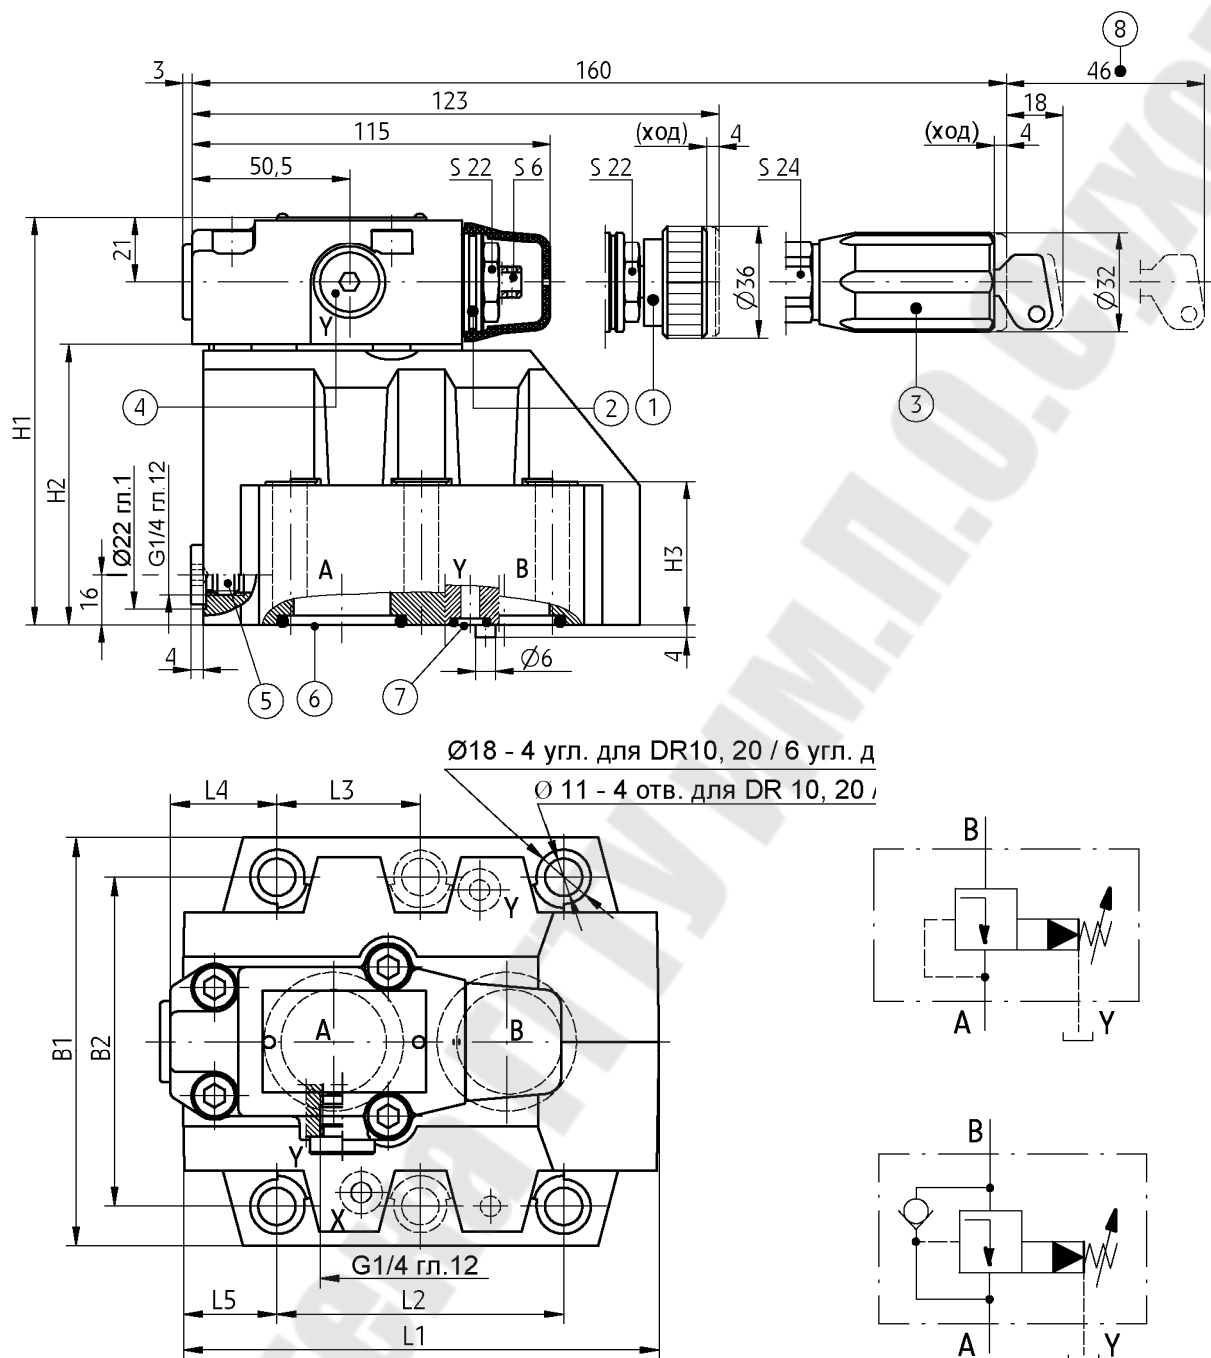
Общий вид, схемы и габаритные размеры редукционного клапана непрямого действия стыкового монтажа типа DR...
